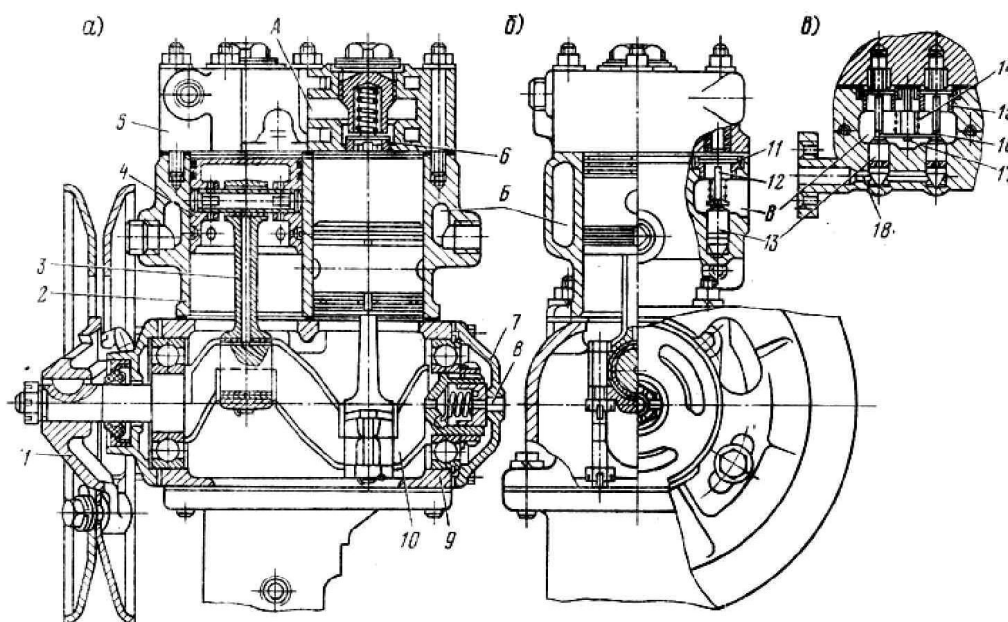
Компрессор пневматического привода тормозов автомобиля ЗИЛ-130
